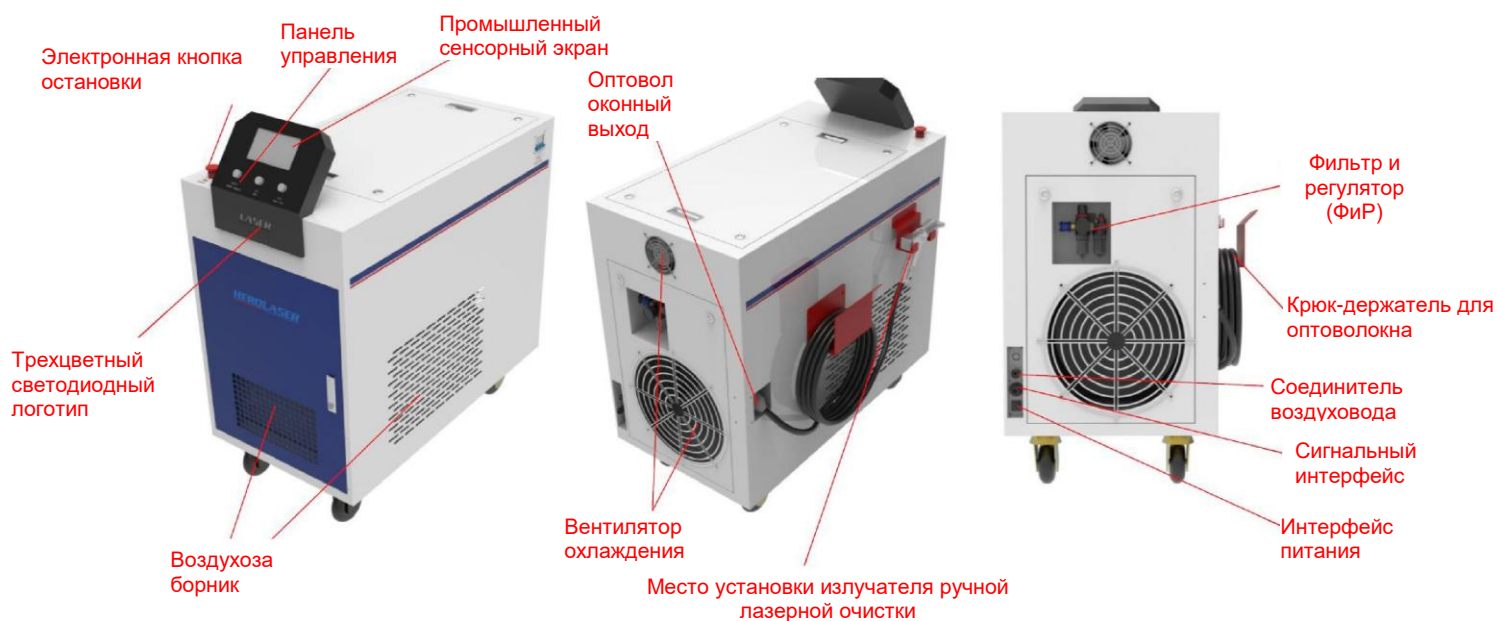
Схема внешней конструкции установки лазерной очистки
